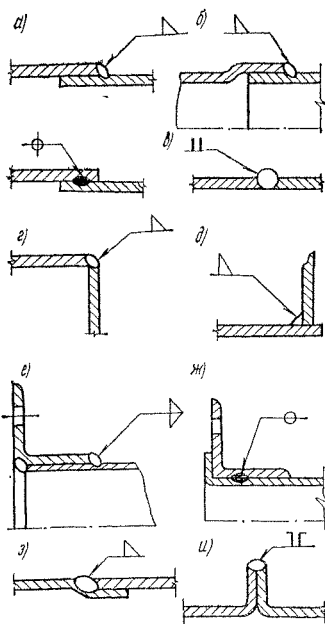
Виды сварных соединений, применяемых при сварке металлических воздуховодов
